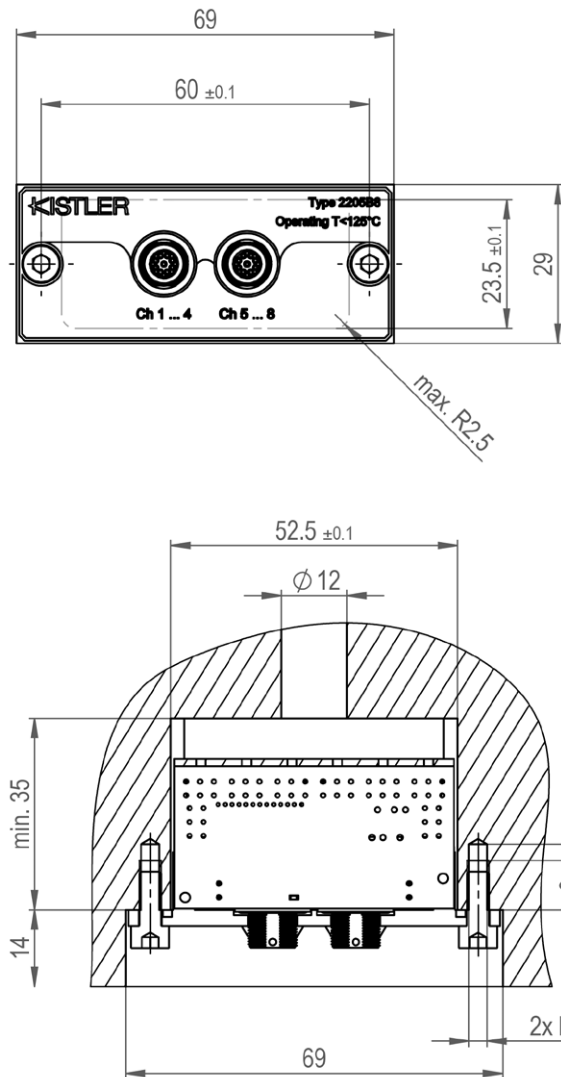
Abmessungen und Einbaumasse – 8-Kanal
